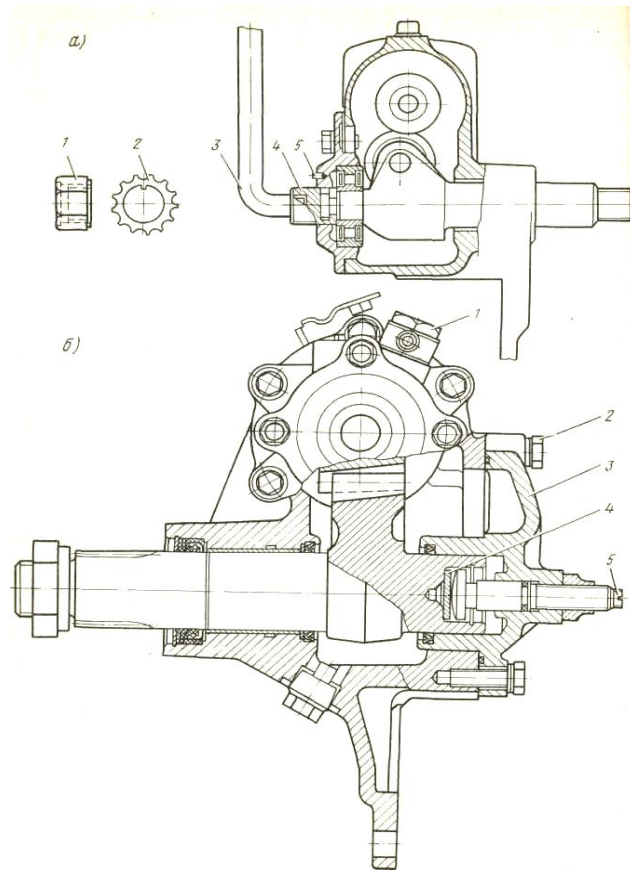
Регулювання рульового механізму автомобілів: а — ГАЗ-53А (1 - ковпачкова гайка; 2 - стопорна шайба; 3 - ключ; 4 - регулювальний гвинт; 5 - стопорний штифт шайби); б - ЗИЛ-130 (1 - пробка заливного отвору; 2 - болт; 3 - кришка; 4 - упорна шайба; 5 - регулювальний гвинт).
